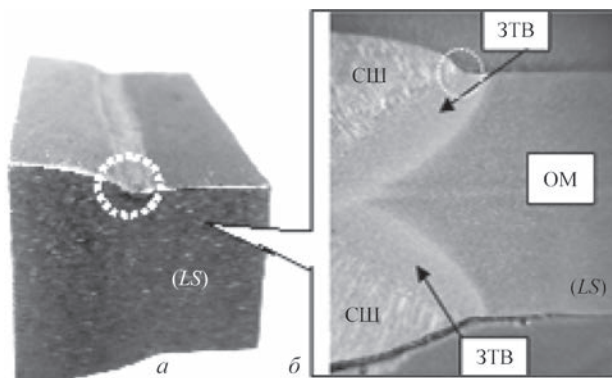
Внешний вид темплета (а), поверхность шлифа после травления в плоскости  $LS$  поперечного сечения (б):  $L$  — направление проката;  $S$  — направление, перпендикулярное к плоскости проката; контуром выделен профиль канавки; СШ — сварной шов; ЗТВ — зона термического влияния; ОМ — основной металл
